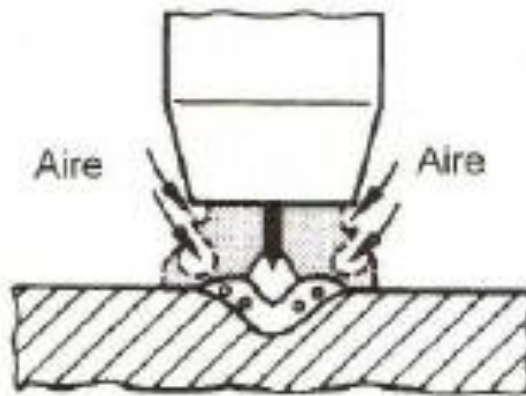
Uso de la polaridad directa en la soldadura de aluminio.
